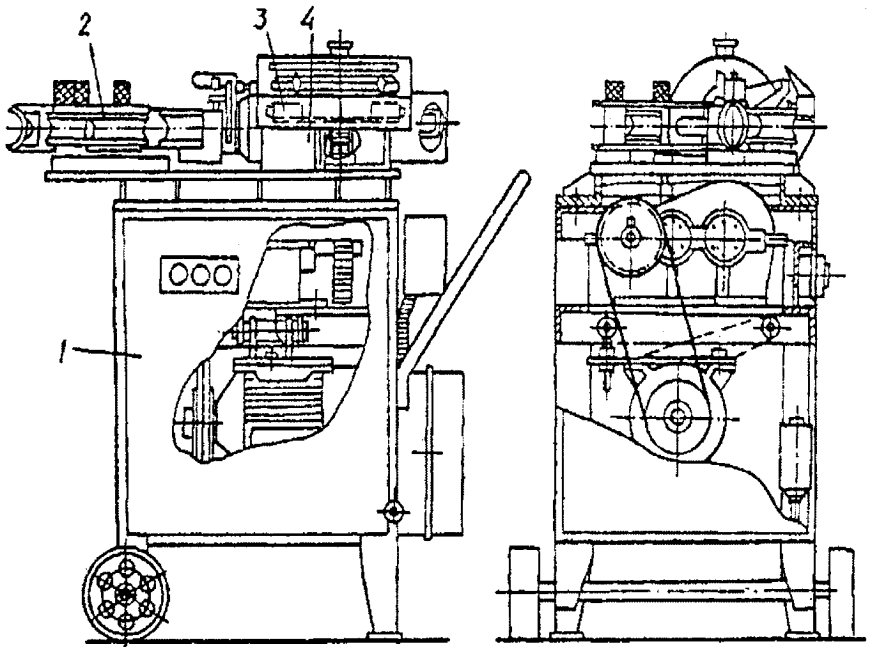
Верстат для згинання труб у холодному стані: 1 — корпус; 2 — змінні пристрої; 3 — механізм налагоджування; 4 — силова частина
